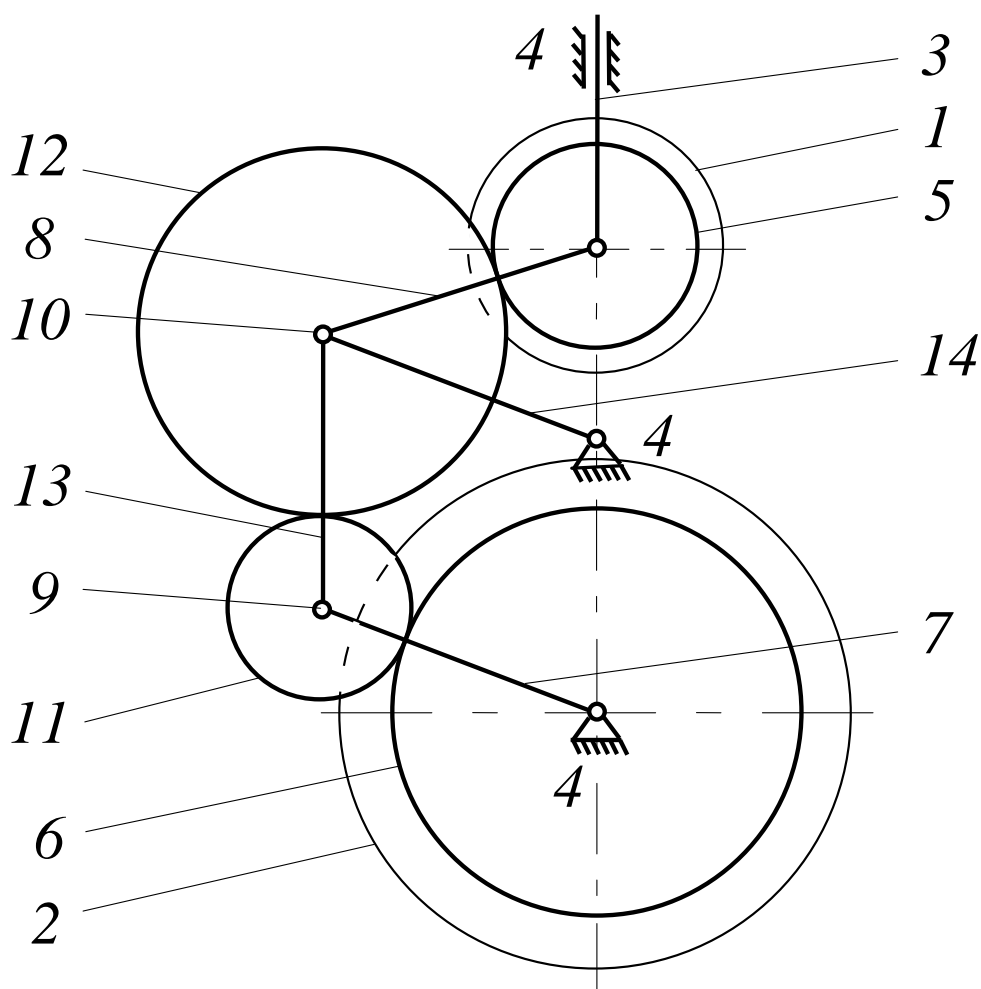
Схема зубчато-рычажного передаточного механизма валов с разными диаметрами
